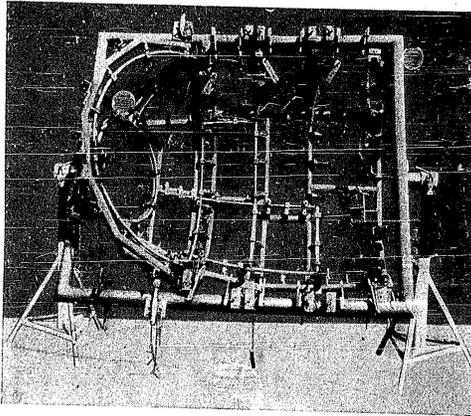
Große schwenkbare Schweißvorrichtung für Dachgerüst. Rechteckiger Rahmen in Rohrbauweise
